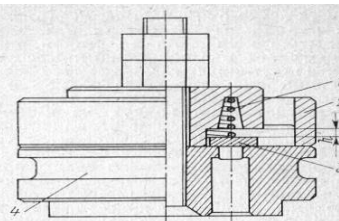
Клапан нагнетательный кольцевой пластинчатый четвертой ступени.
